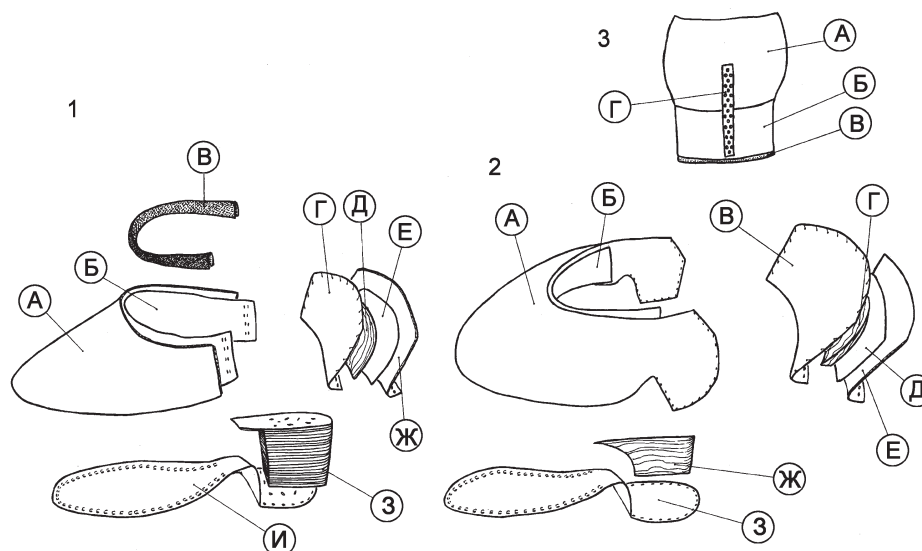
Схемы сборки башмаков. 1 — конструкция с наборным кожаным каблуком: А — головка; Б — поднаряд; В — тканая обшивка; Г — карман задника; Д — деревянный вкладыш; Е — кожаная прокладка; Ж — задник; З — наборный каблук; И — подошва. 2 — конструкция с деревянным каблуком: А — головка; Б — поднаряд; В — карман задника; Г — берестяной вкладыш; Д — кожаная прокладка; Е — задник; Ж — каблук; З — подошва. 3 — реконструкция башмаков, вид сзади: А — задник; Б — обтяжка деревянного каблука; В — подошва; Г — декоративная накладка
